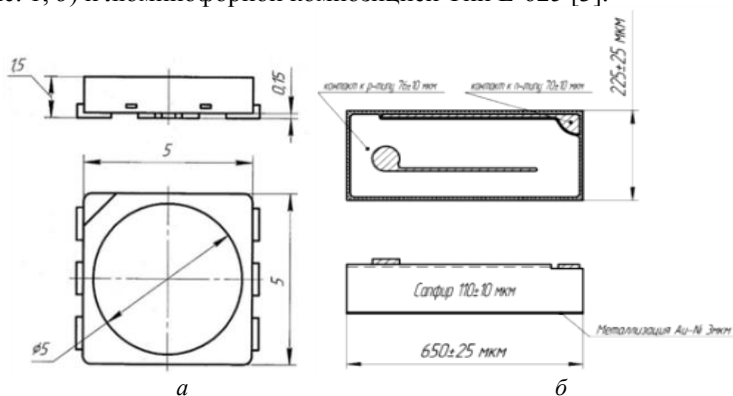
Габаритный чертёж корпуса светодиода (а) и геометрия светодиодного кристалла (б)
